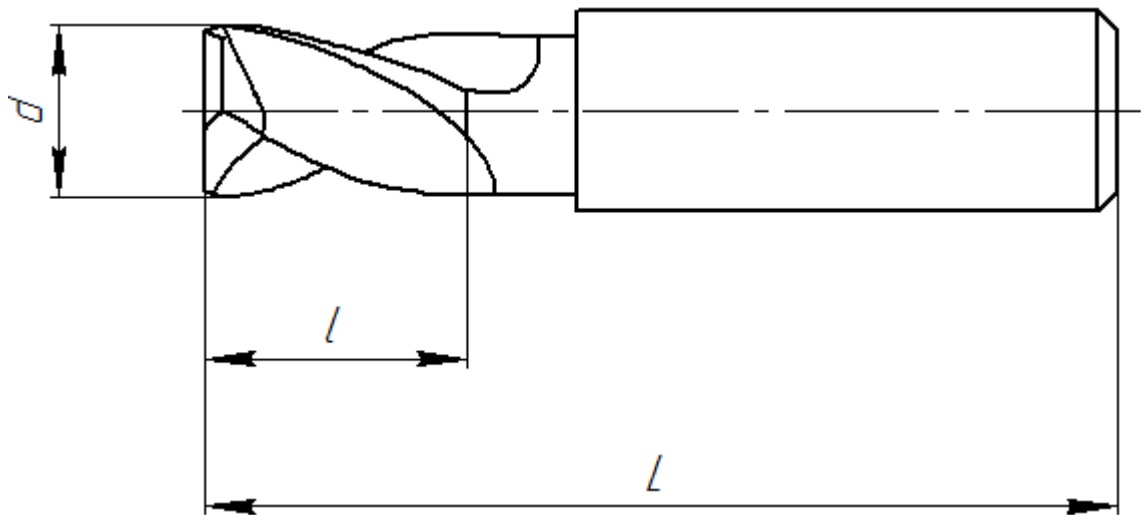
Шпонкова цільна твердосплавна фреза по ГОСТ 16463-80
